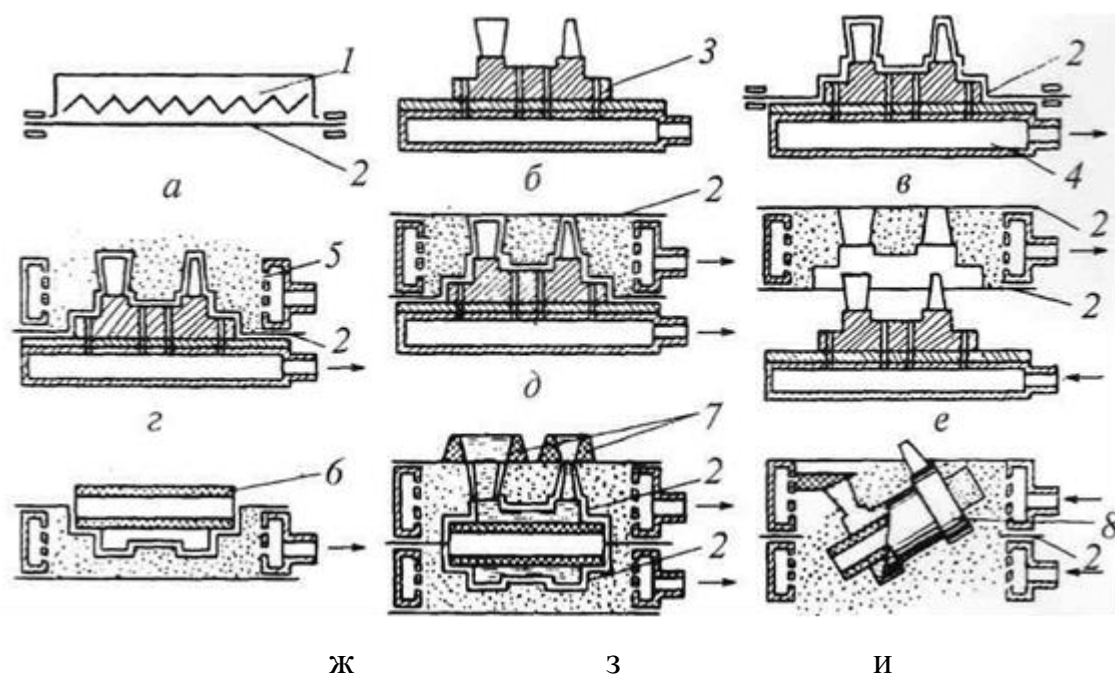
Схема вакуумно-плёночной формовки: 1нагревательное устройство; 2-плёнка; 3-модель; 4и5 плита и опока с вакуумированными полостями; 6-стержень; 7-наращалки;8-отливка; а-нагрев плёнки; б-модельная оснастка; в-обтягивание оснастки плёнкой;г-засыпка опоки песком; д-накрытие опоки плёнкой и вакуумирование; е-протягивание модели; ж-установка стержня; з-заливка формы металлом; и-выбивка
